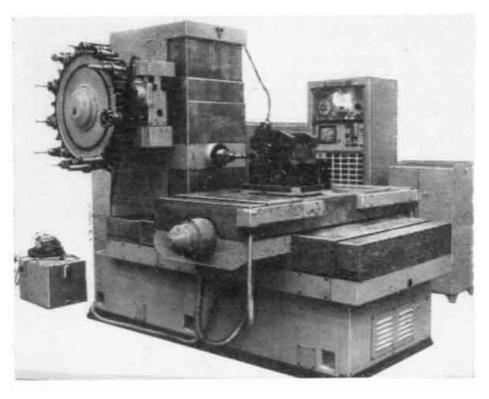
Горизонтальный станок с магазином типа «PYKA» и барабаном с инструментами
